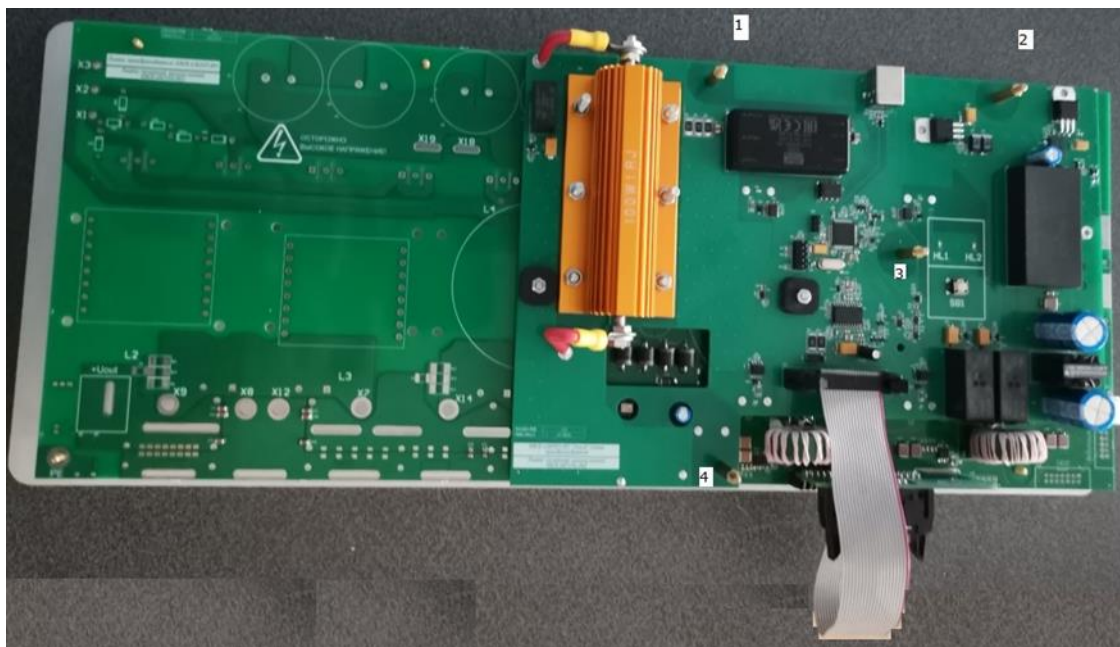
Проверяемая плата в сборе с платой стенда преобразователя
